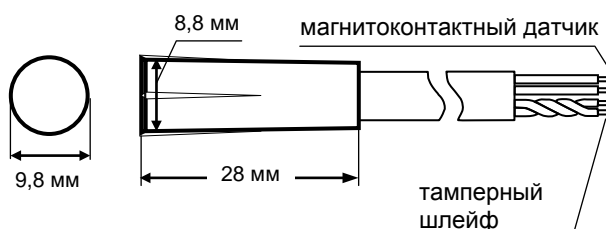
Геркон извещателя S-2 в пластмассовом корпусе
